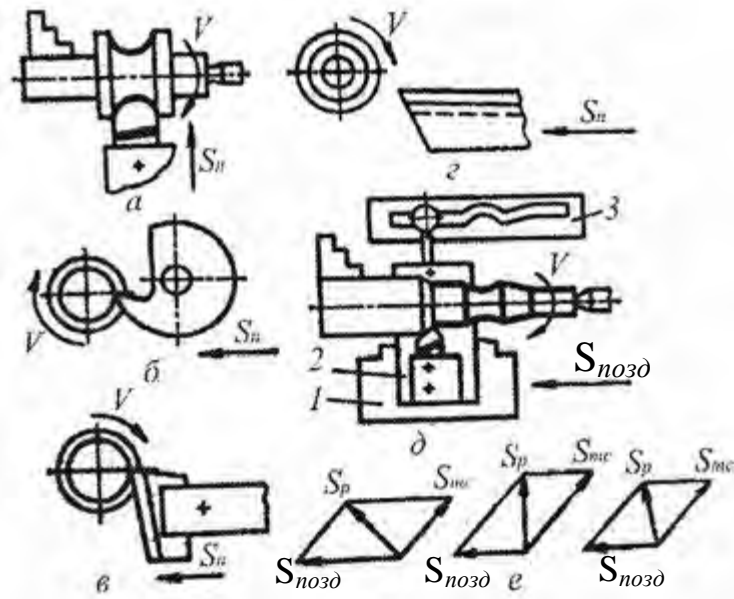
Схеми оброблення фасонних поверхонь на токарно-гвинторізних верстатах
